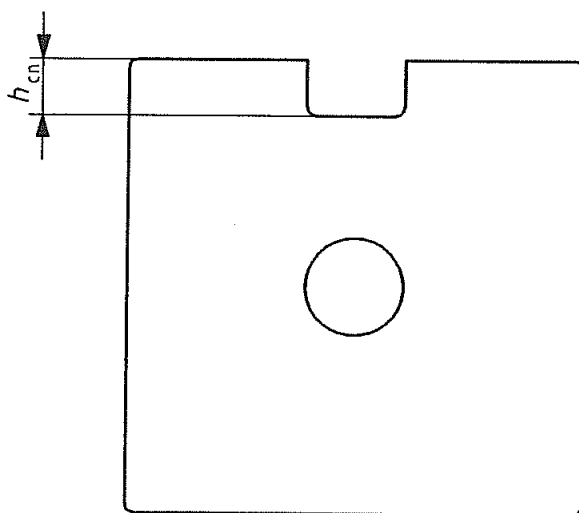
Шаблон для настройки приборов для измерения высоты профиля резьбы
